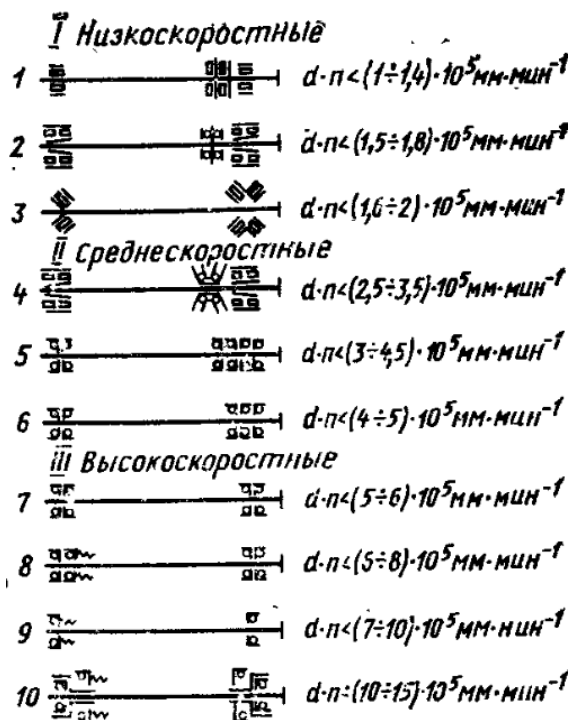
Типовые конструктивные схемы установки опор ШУ
